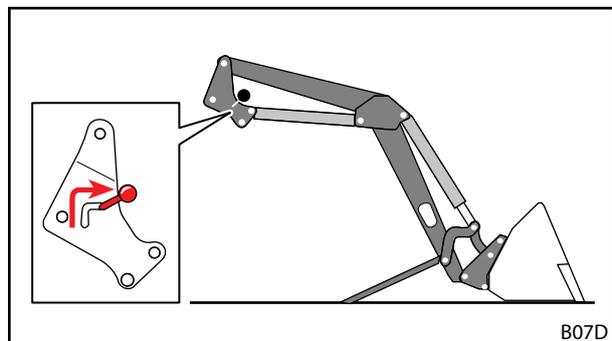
Apertura del dispositivo di blocco del caricatore frontale
